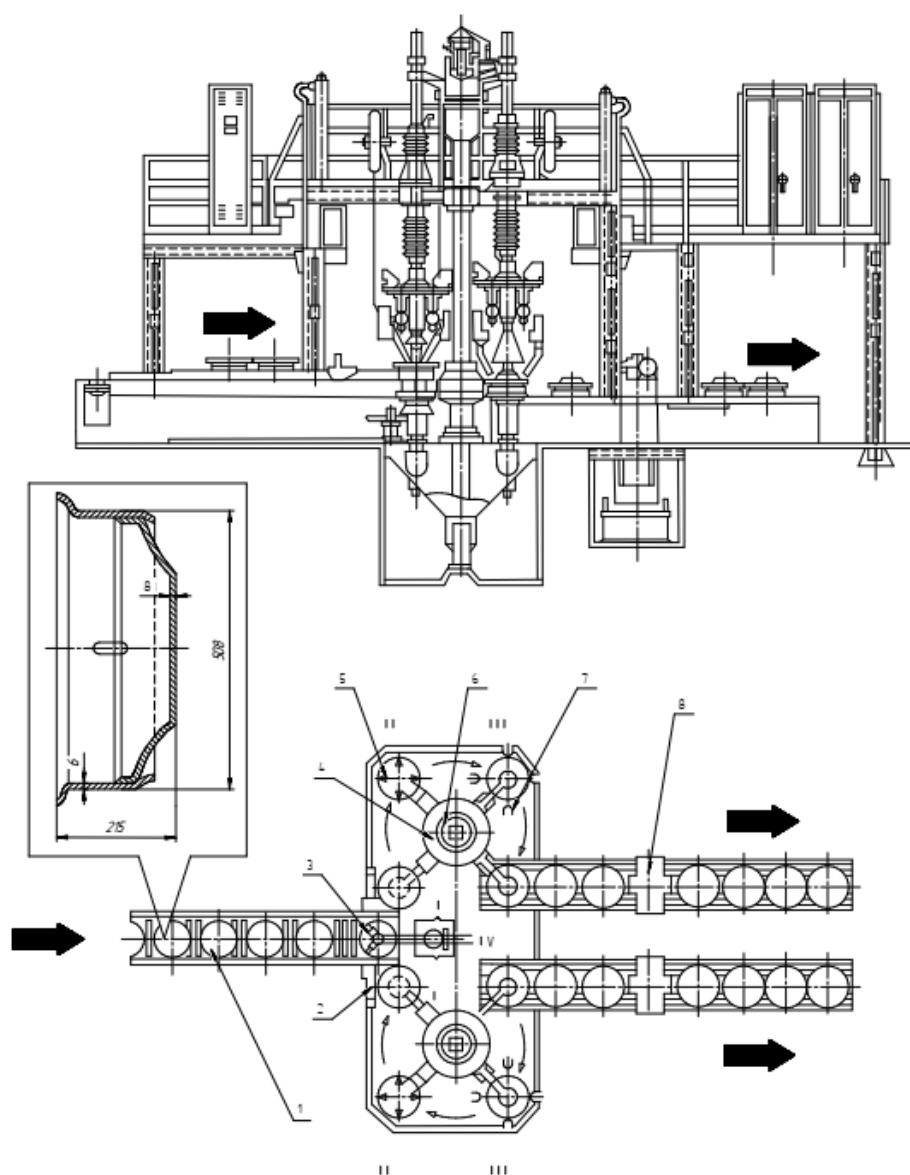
Схема багатопозиційної установка автоматичного зварювання колеса
